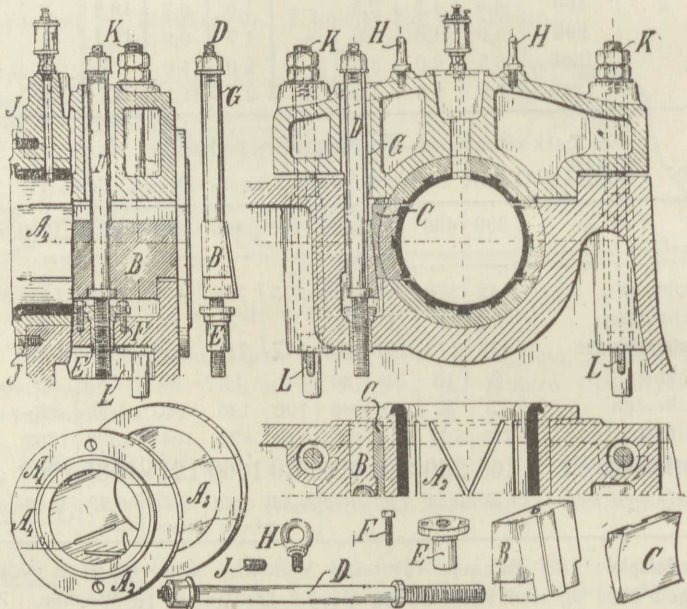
Hauptlager für Maschinen über 900 Hub.
